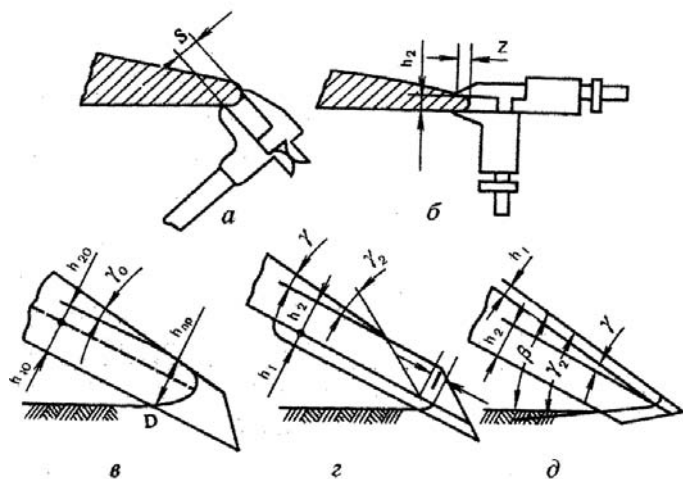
Схемы лезвий почворезущих деталей и методов их контроля: а – контроль ширины затылочной фаски S ; б – контроль толщины h_2 режущей кромки на расстоянии Z от вершины; в – однородное затупляющееся лезвие; г, д – самозатачивающиеся лезвия с нижним и верхним расположением режущего (наплавленного) слоя; γ_1 – угол клина однородного лезвия; h_{np} – предельная толщина однородного лезвия; h_{10} – условная толщина нижнего слоя однородного лезвия; h_{20} – условная толщина верхнего слоя однородного лезвия; h_1 – толщина режущего слоя самозатачивающегося лезвия; h_2 – толщина несущего слоя самозатачивающегося лезвия; γ – угол клина самозатачивающегося лезвия; γ_2 – угол самозатачивания; β – угол крошения
